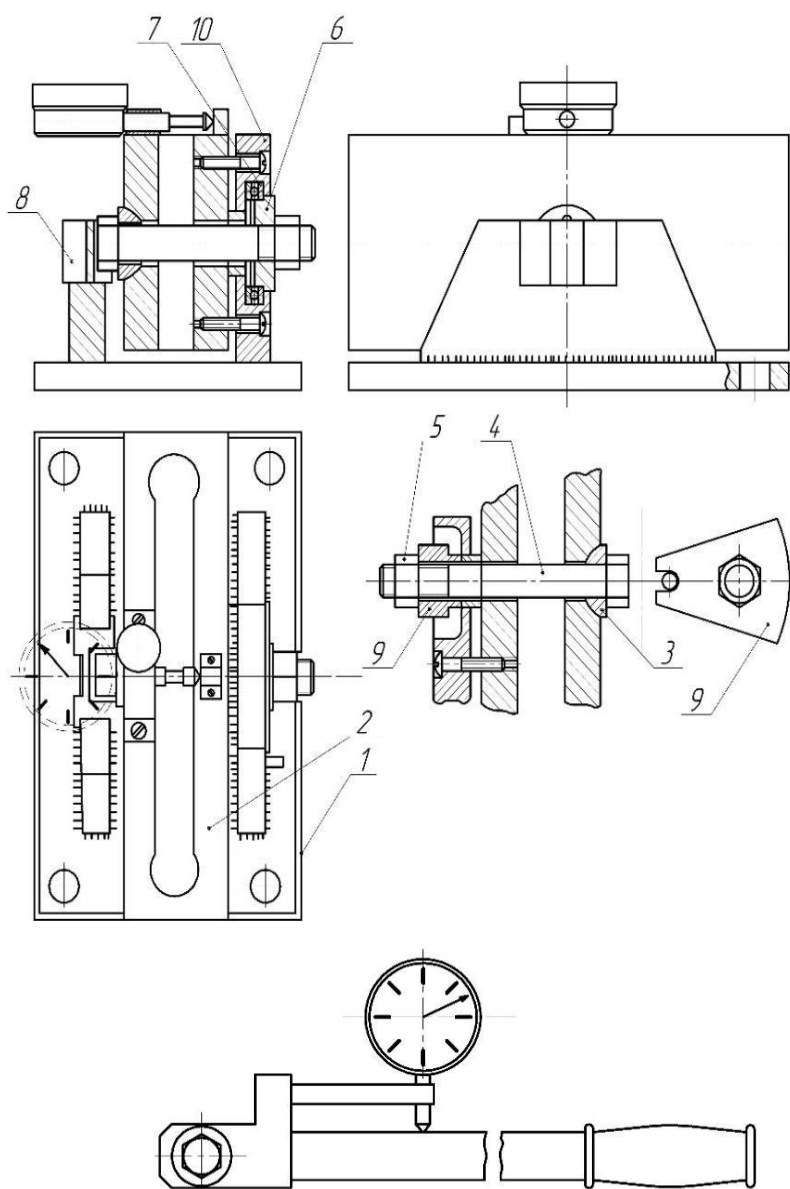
Схема установки ДМ-27: 1 – корпус; 2 - динамометрична пружина; 3 - сферична шайба; 4 - досліджуваний болт; 5 – гайка; 6 – втулка; 7 - упорний підшипник; 8 - змінний сухар; 9 – обмежувач; 10 - кріпильні гвинти.
